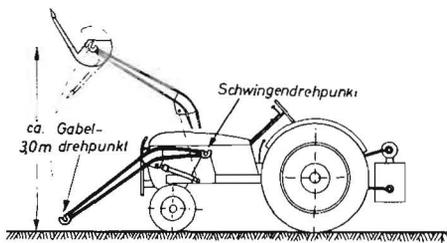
Prinzip des Frontladers und Kennzeichnung wesentlicher Teile
